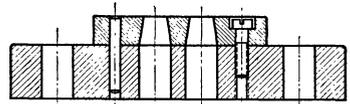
Befeestigung der Schnittplatte durch Schrauben und Paßstifte.
